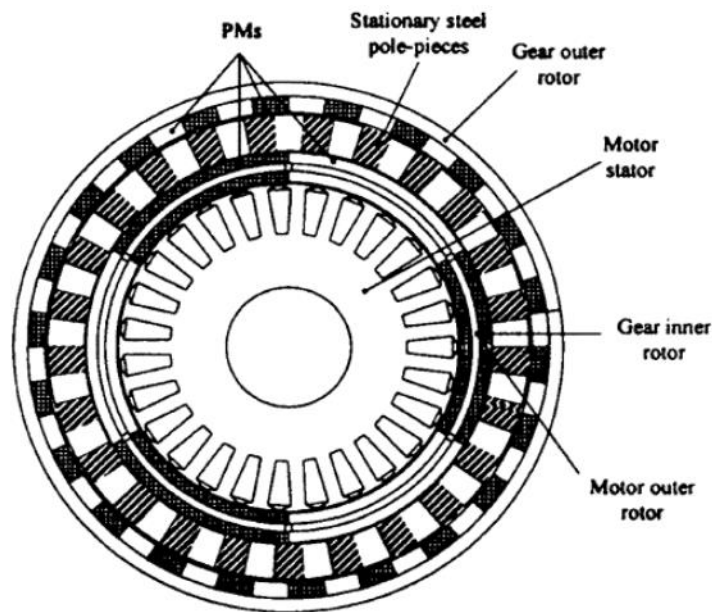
Magnetic Geared PM Machine (con rotore esterno). [19]
